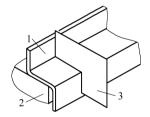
检查工件角度 1—工件 2—平台 3—样板
